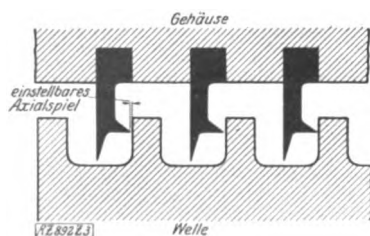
C. A. Parsons & Co., Ltd., Dichtungsringe der Ausgleichkolben.
